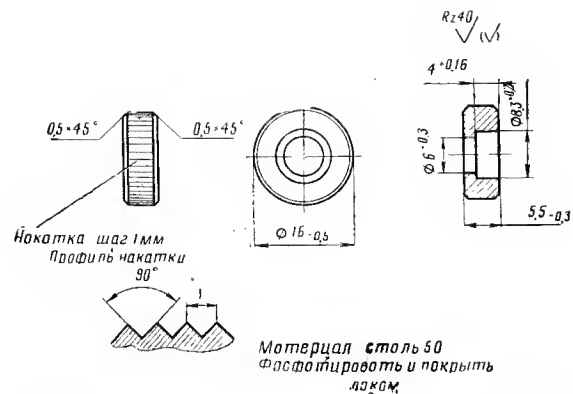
Втулка соединительного винта 56-A-212.8-3
